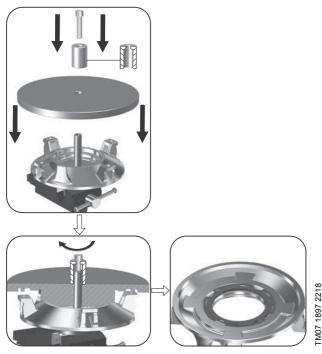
Уплотнительное кольцо, стопор уплотнительного кольца и всасывающий узел, установленные в приспособлении L
